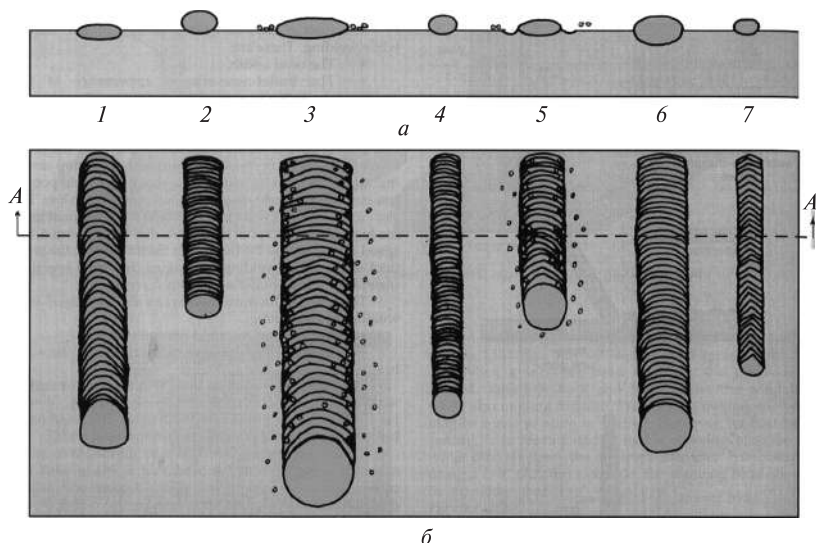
Влияние параметров режима сварки на качество формирования шва при ручной дуговой сварке:
